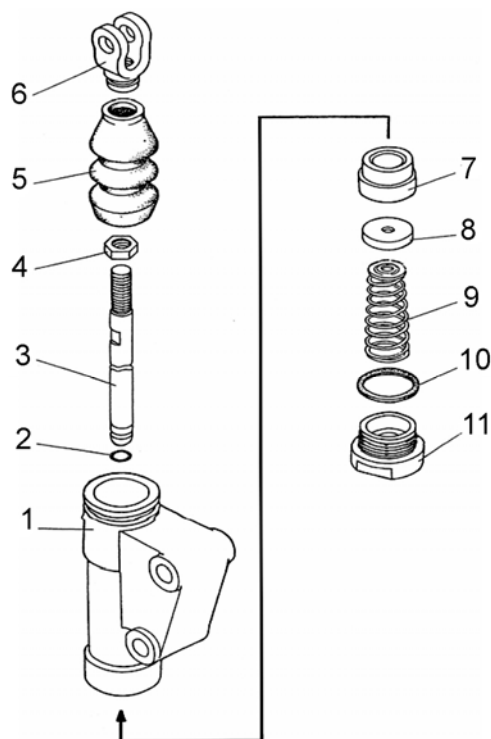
Цилиндр главный управления сцеплением на реверсе
